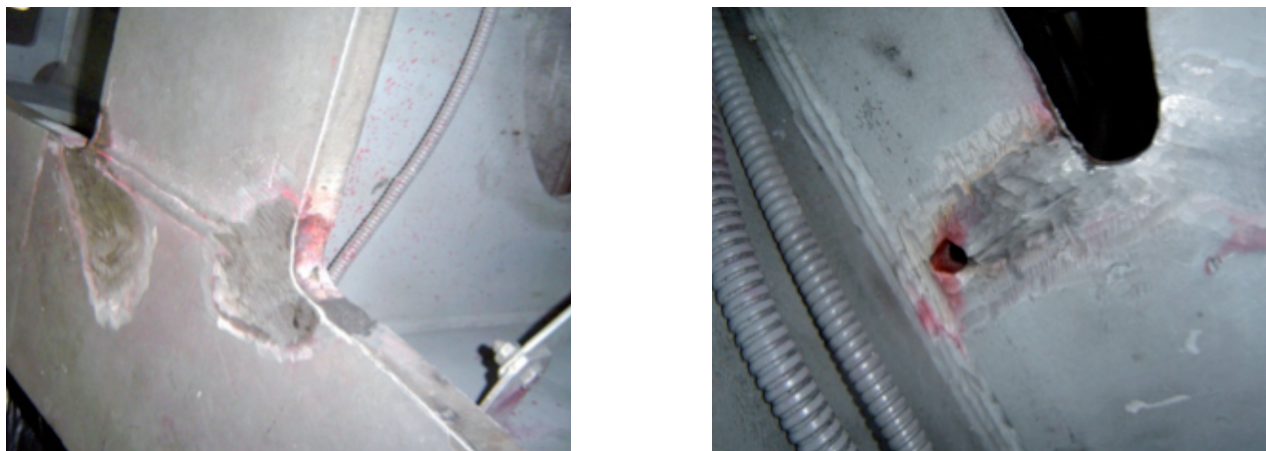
Detalle zona reforzada mediante soldadura en bastidor de MADE AE61.
